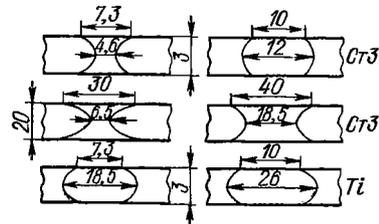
Размеры растекания сварочного тока по стальным и титановым листам
